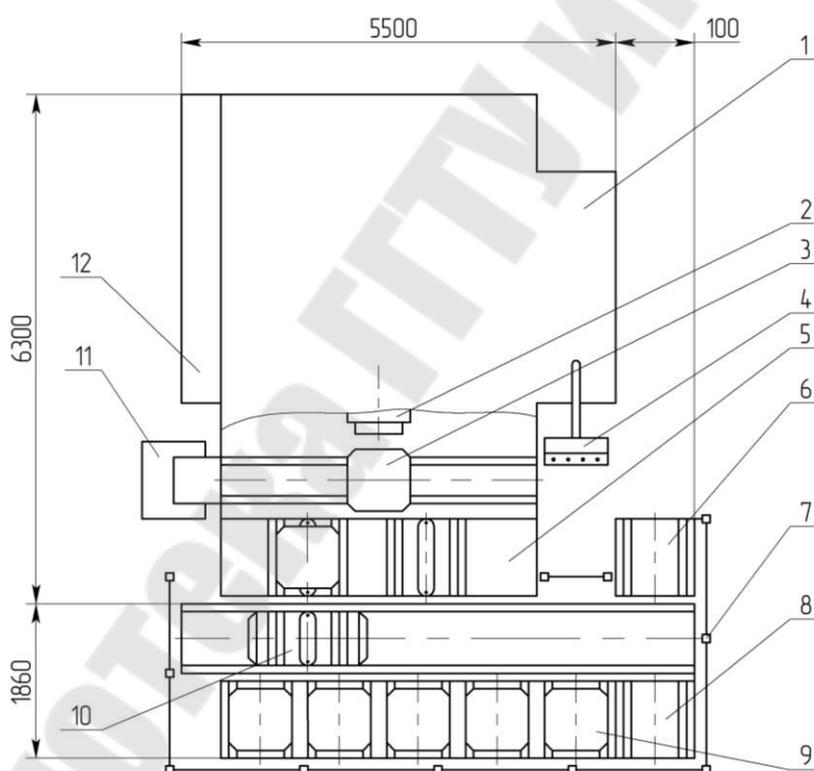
Пример планировки АТК для обработки корпусных деталей.
